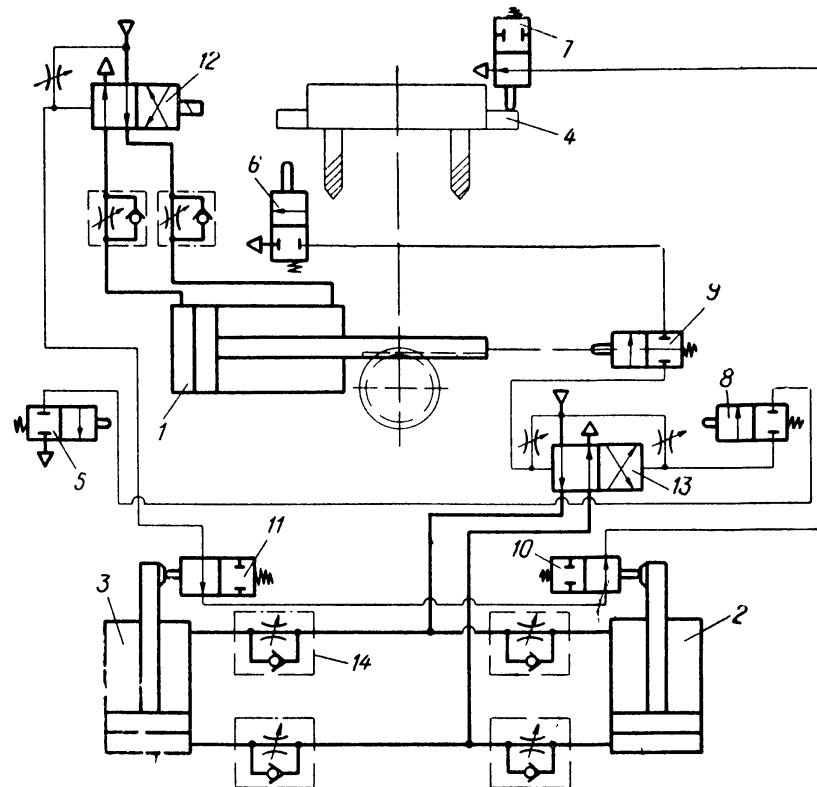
Принципиальная схема пневмосистемы вертикально-сверлильного станка
